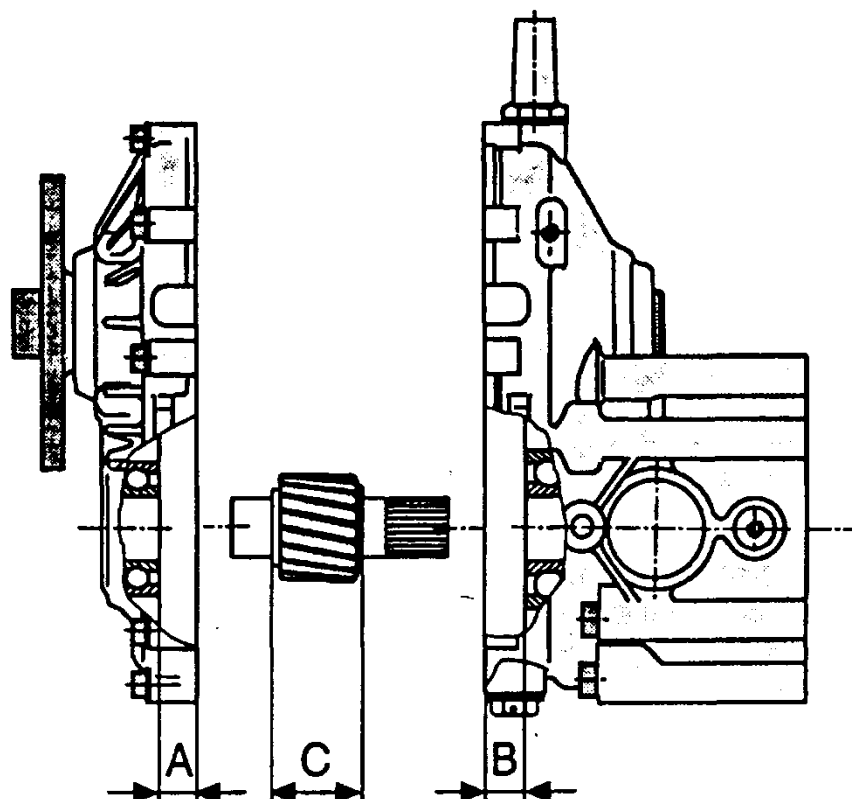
Определение осевого зазора между ведущей шестерней и подшипником
